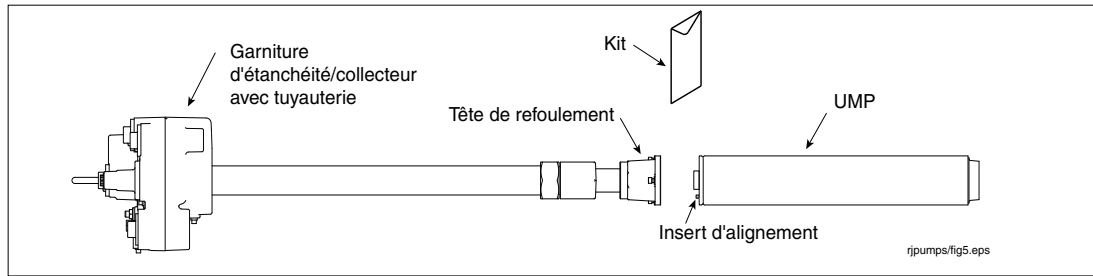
Fixation de garniture d'étanchéité/collecteur avec tuyauterie à l'UMP
